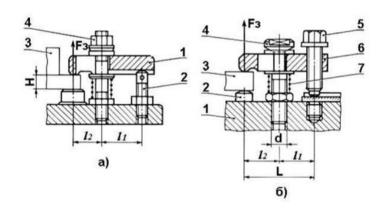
Комбинированные винтовые зажимы: а) нормализованный винтовой прихват с передвижной прижимной планкой (1 — прижимная планка; 2 — регулируемая опора; 3 — деталь; 4 — нажимная гайка); б) нормализованный винтовой прихват (1 — корпус приспособления; 2 — опора; 3 — деталь; 4 — головка винтовой опоры; 5 — нажимной винт; 6 — прижимная планка; 7 — пружина).
